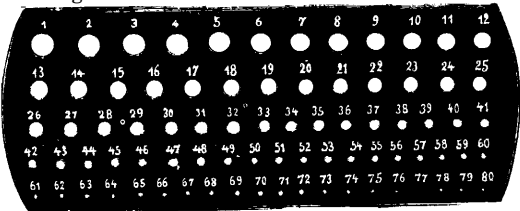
Gläsermaß und Glasrand-Fräsmaschinen
